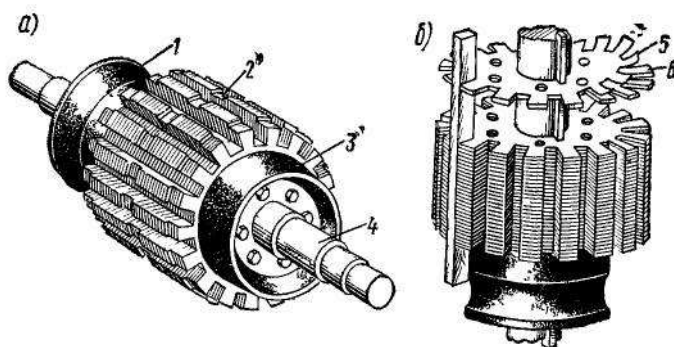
Сердечник якоря (а) и процесс его сборки (б):
